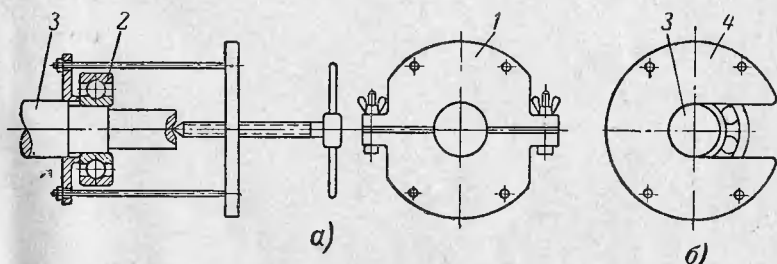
Винтовые съемники для демонтажа подшипника с вала.
